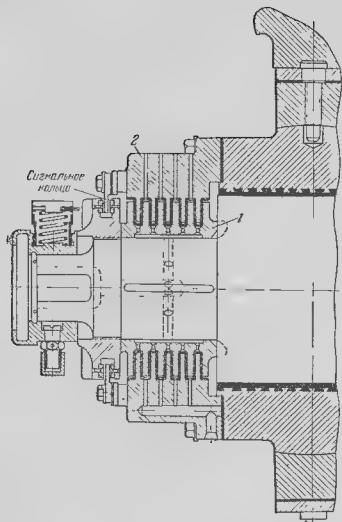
Упорный подшипник турбины ХТЗ.
